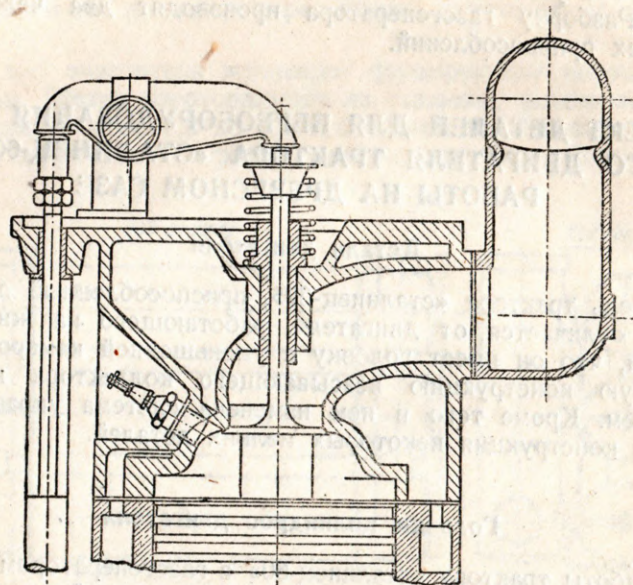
Головка двигателя трактора «сталинец-60» для работы на древесном газе
